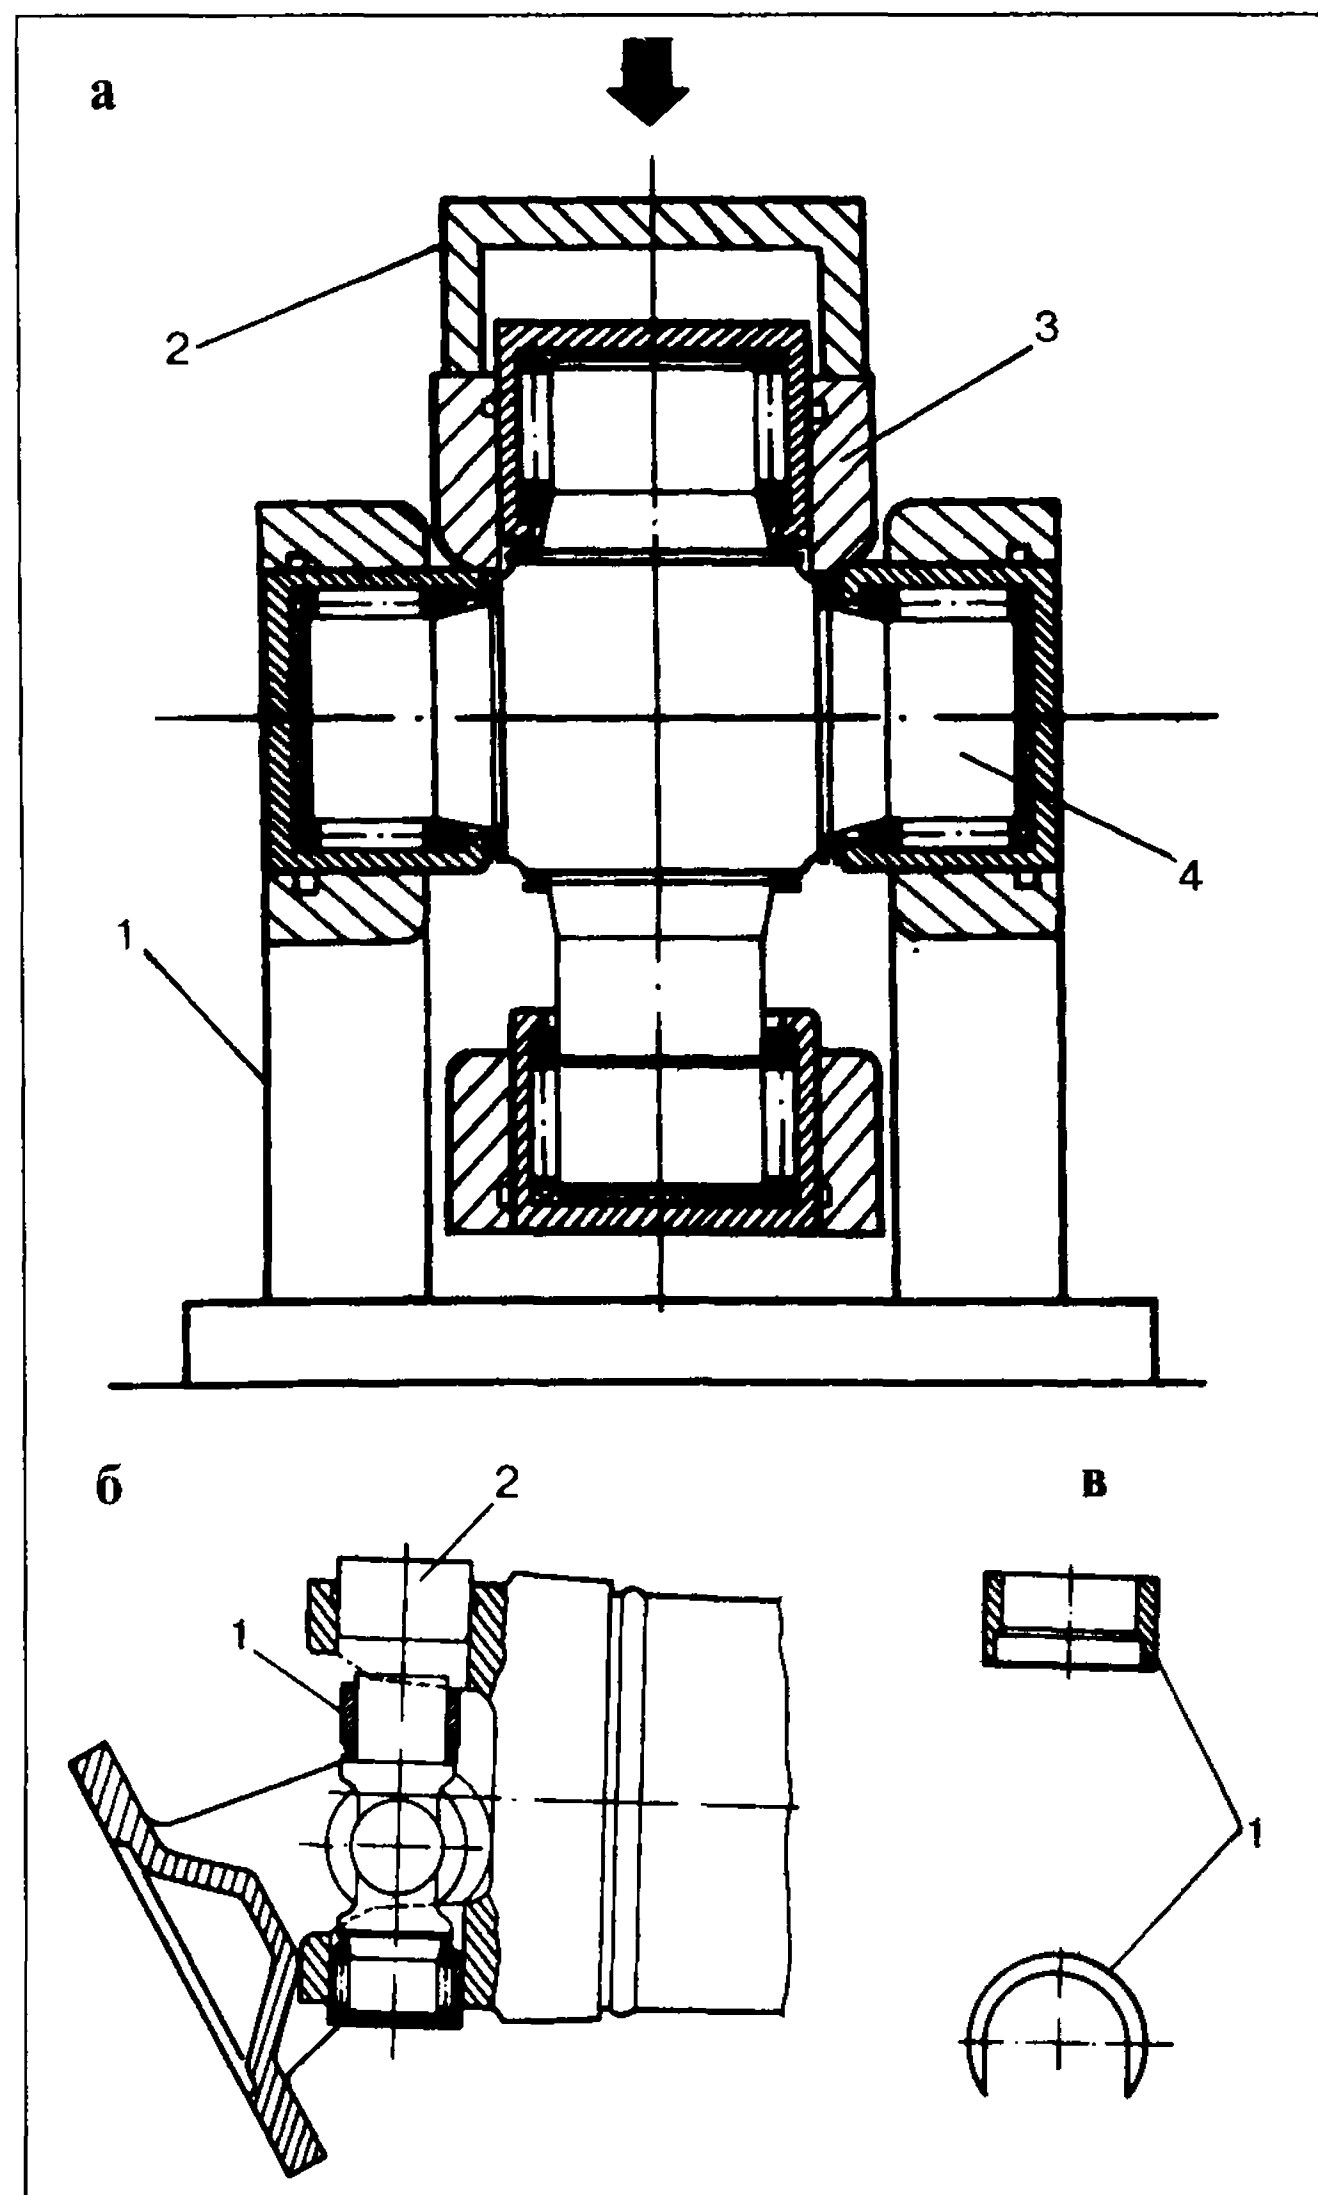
Выпрессовка подшипников крестовины из вилок карданного шарнира:
